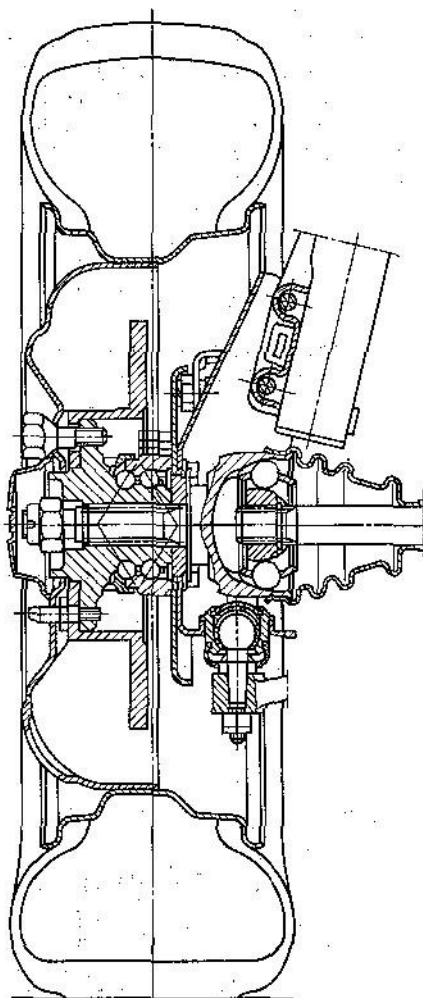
Радиально-упорный шариковый подшипник фирмы СКФ, устанавливаемый в передней оси автомобиля «Фиат-панда». Неподвижный шарнир равных угловых скоростей расположен довольно точно на оси поворота. На уступе корпуса шарнира установлено центробежное кольцо, дополнительно предотвращающее проникновение воды и грязи. Наружное кольцо подшипника крепится болтами к опоре подшипника колеса, изготовленной из листового материала
